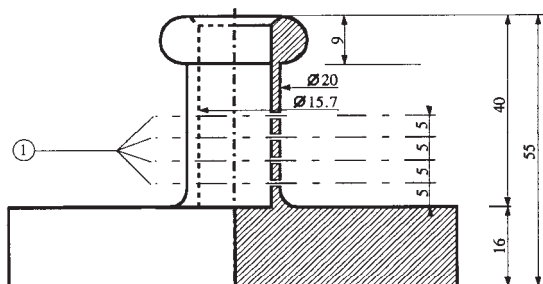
Полый бронзовый цилиндр, закрытый с одной стороны; чертеж и размеры детали в мм
